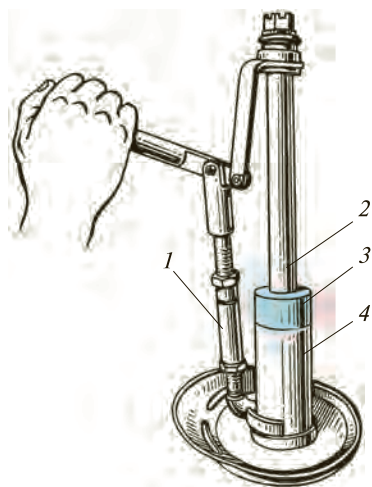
Выпрессовка манжеты с уплотнительным кольцом в сборе со штоком из резервуара:
